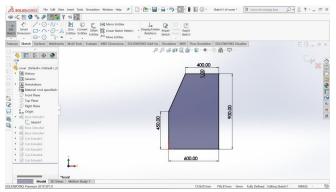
Desain 3 Dimensi rangka besi Hollow
